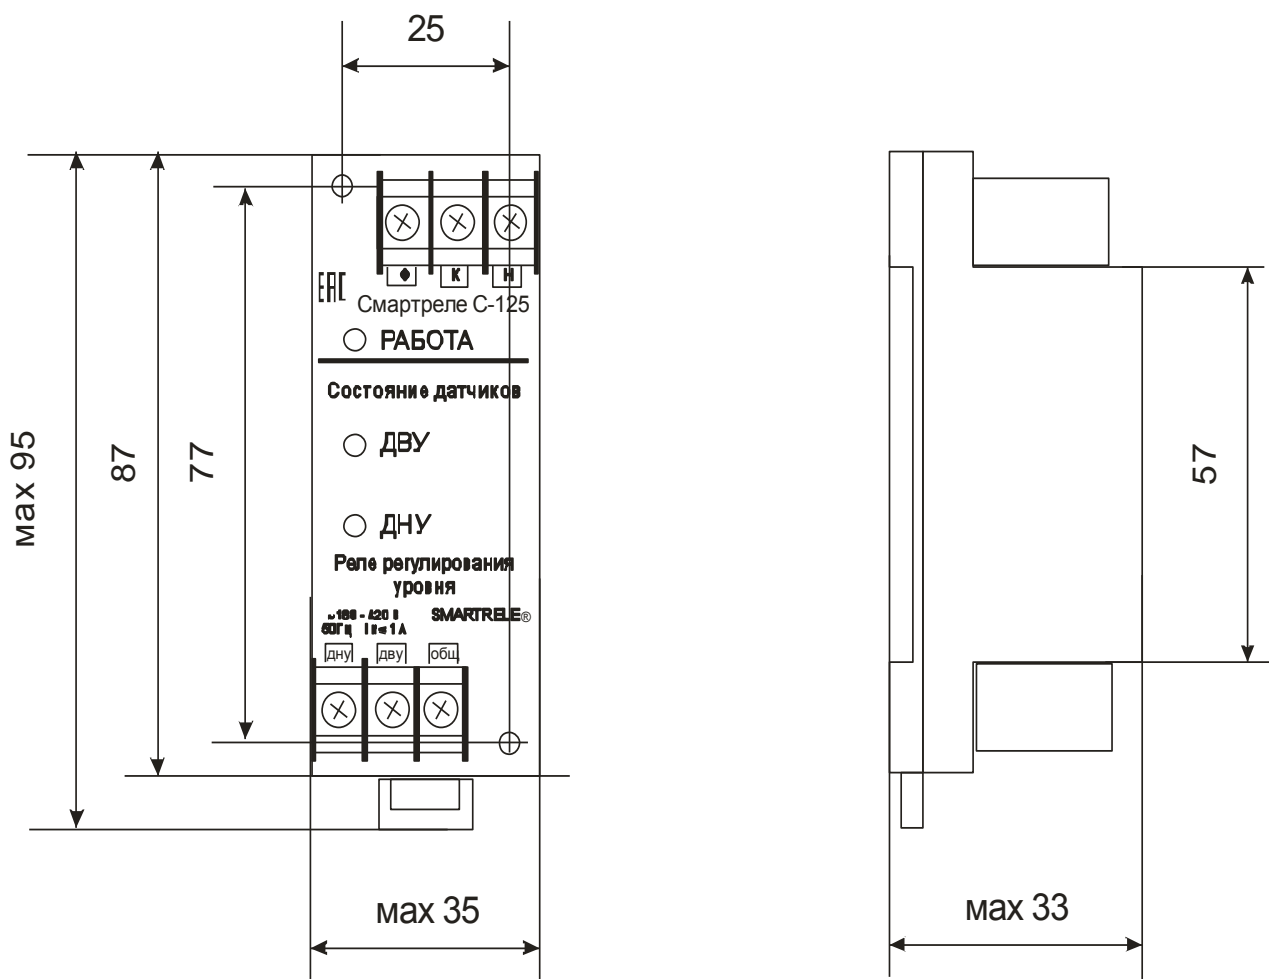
внешний вид, габаритные и установочные размеры СМАРТРЕЛЕ С-125
